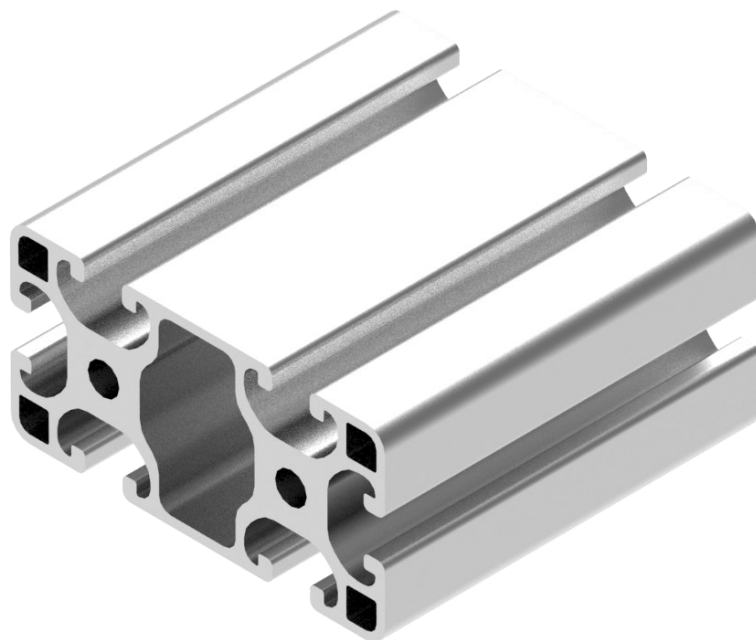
Item24 - Sezione Profilo 8 80x40
